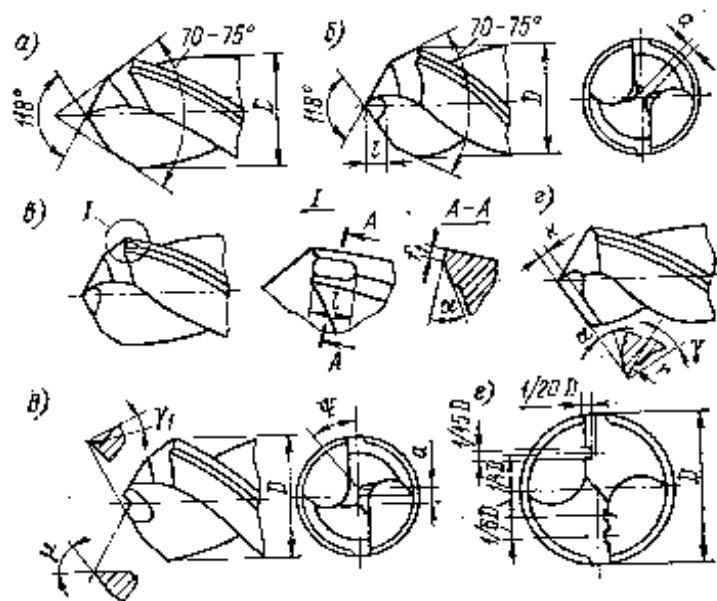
Форми заточування ріжучих кромок спіральних свердел
